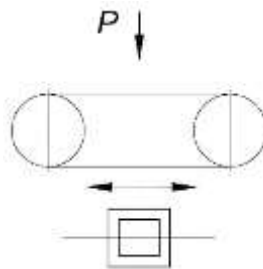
Схема різання заготовки на стрічковій пилі
